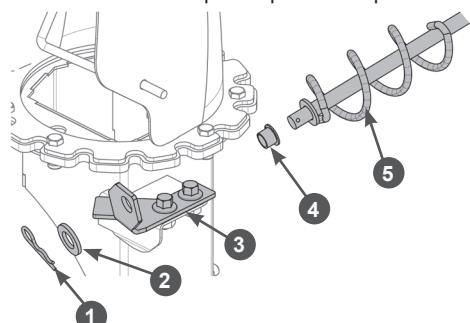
Установка рычага управления поворотом жёлоба (сторона жёлоба)
